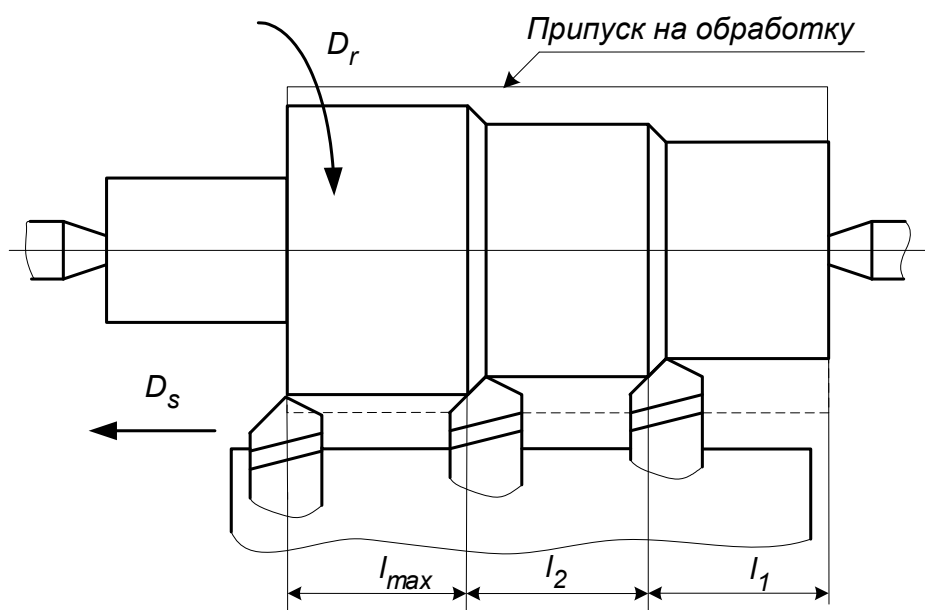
Схема токарной многорезцовой обработки ступенчатого вала
